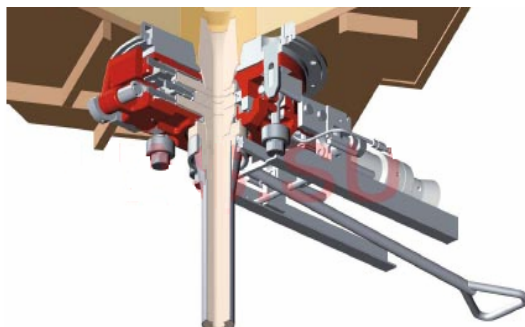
Схема подачі сталі з ПК через трохплітний шибєрний затвор
